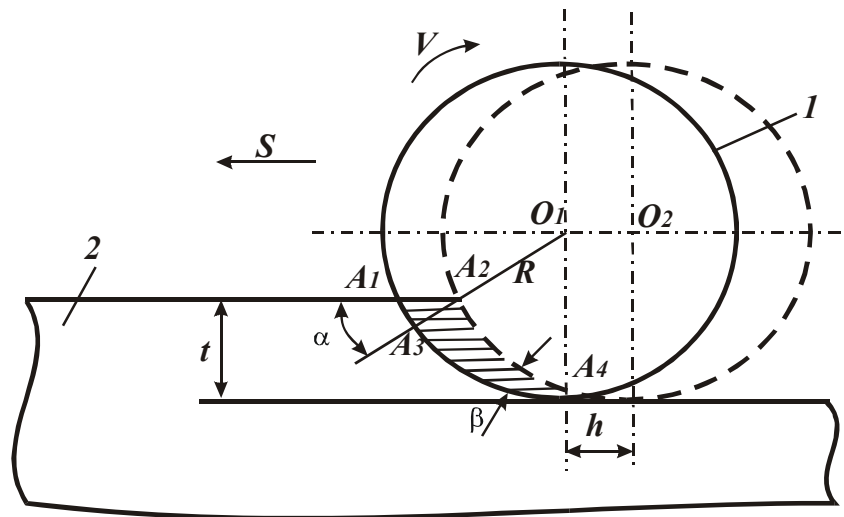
Розрахункова схема циліндричного фрезерування:
